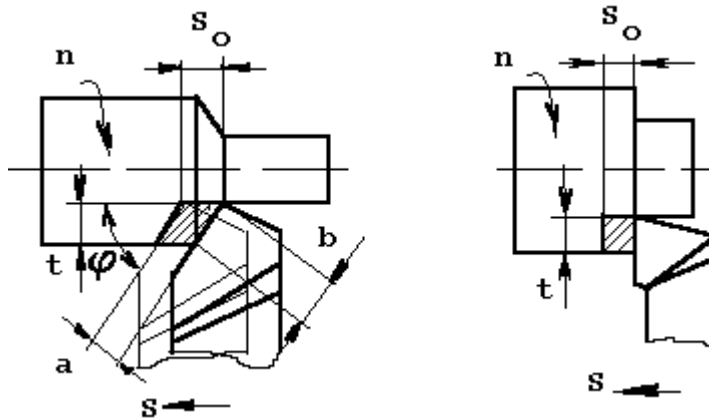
Геометрия и размеры слоя металла, срезаемого резцом:
